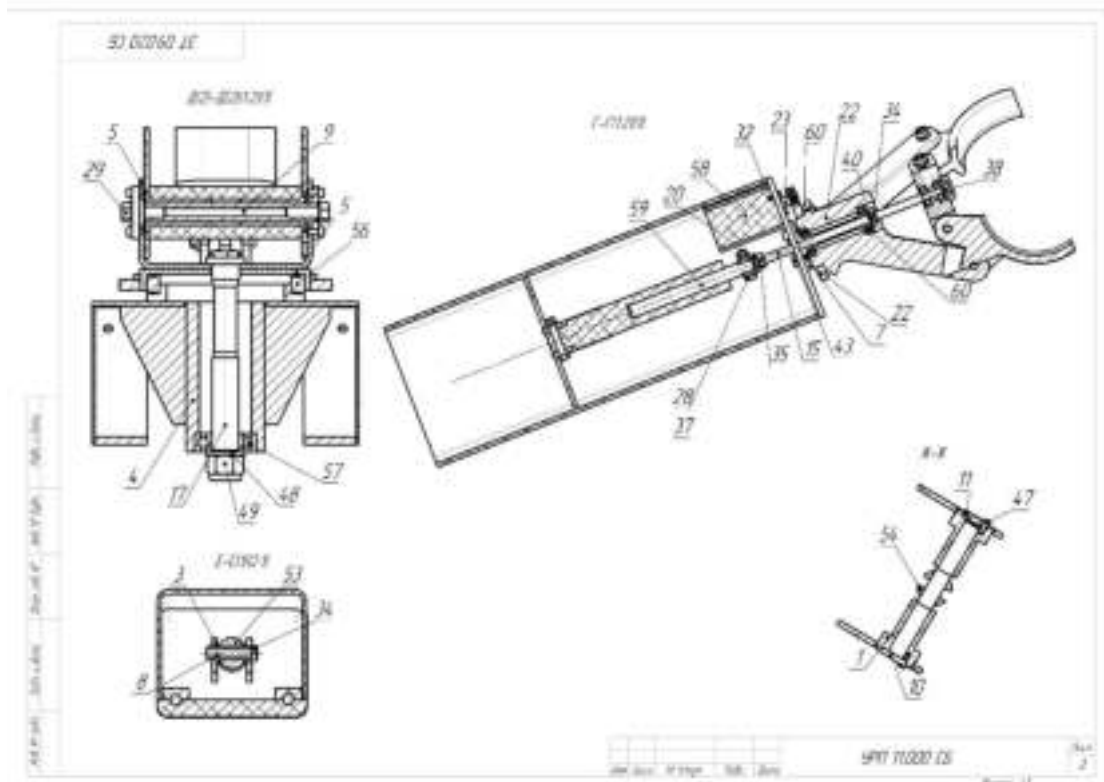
Фрагмент сборочного чертежа захвата
